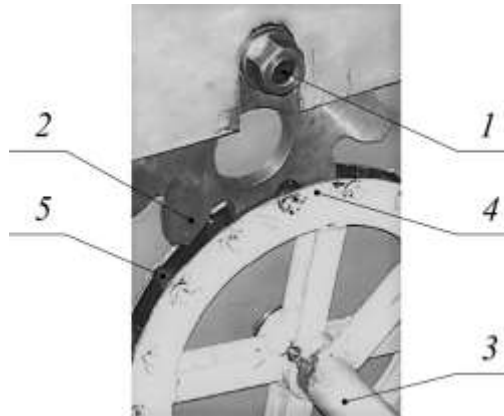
Цівкова передача (вид загальний): 1 – ведучий вал; 2 – зубчасте колесо; 3 – ведений вал; 4 – цівкове колесо; 5 - цівки
